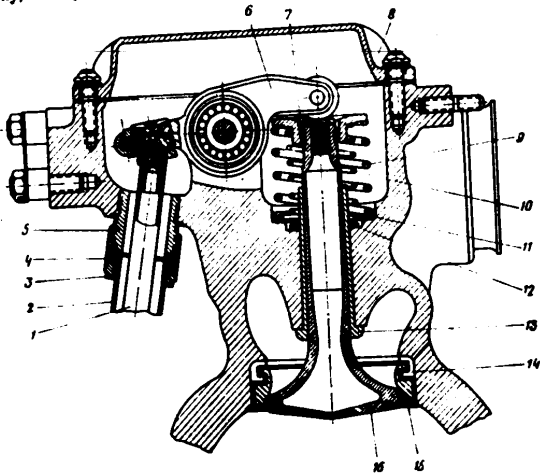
Рычаг клапана, собранный в цилиндре (вид сверху).
